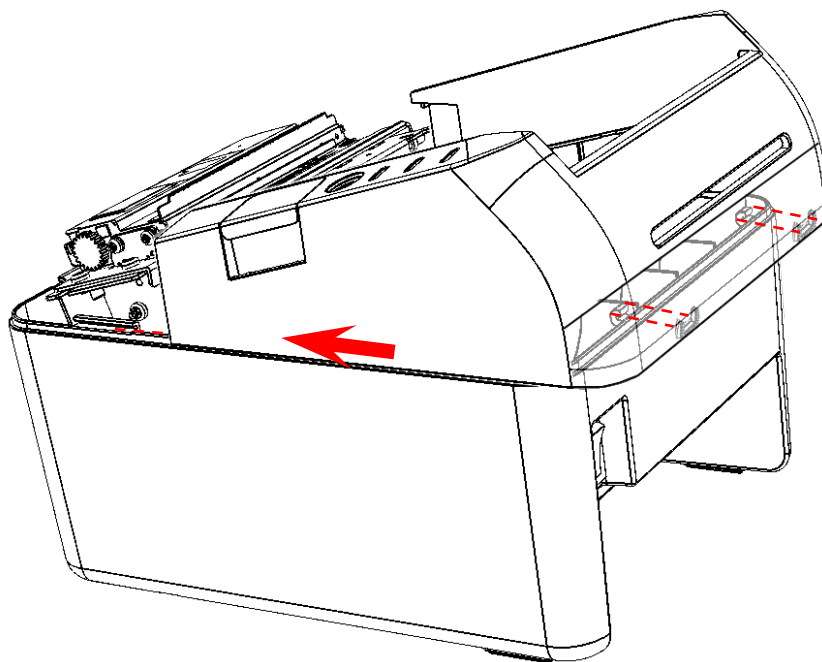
Установка верхней части корпуса ККТ на его нижнюю часть
